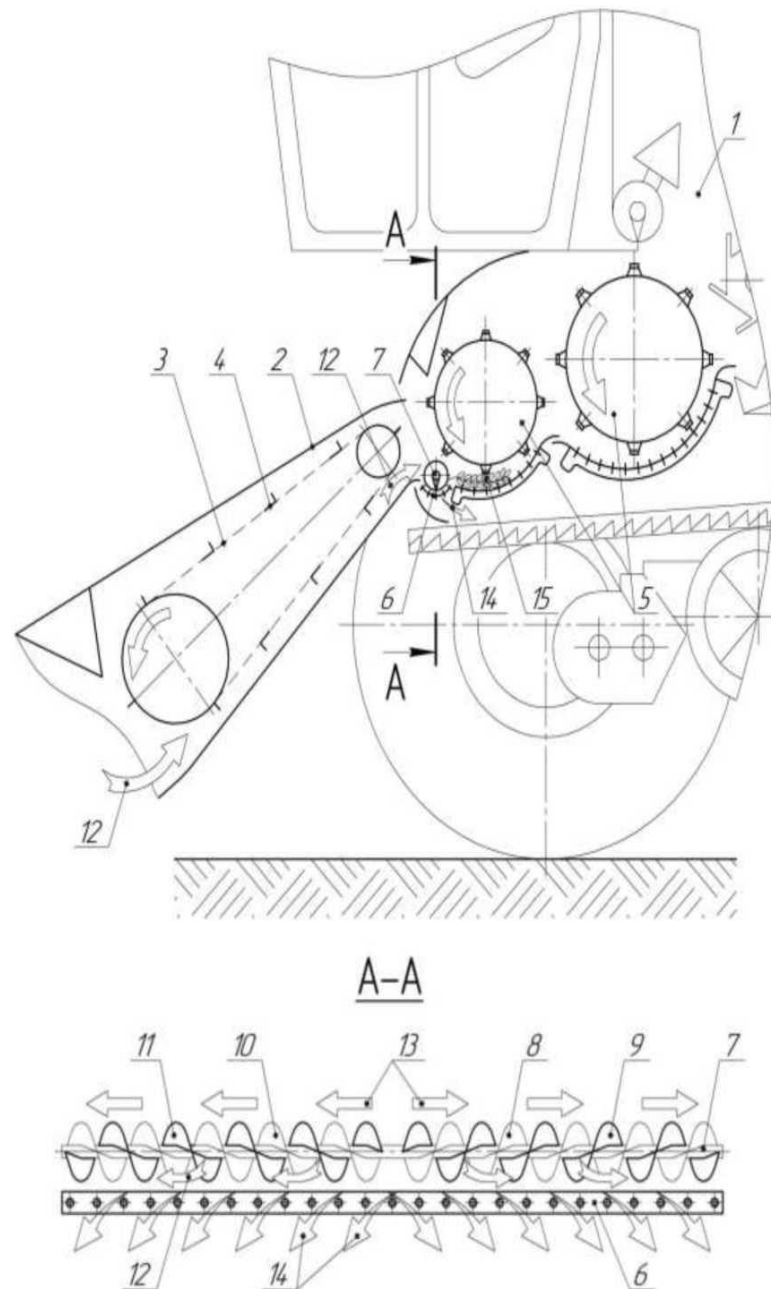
Зернозбиральний комбайн, з пристроєм для попереднього виділення вільного зерна: 1 – комбайн; 2 – похила камера; 3 – транспортер; 4 – скребок; 5 – молотарка; 6 – сепаруюча решітка; 7 – шнек; 8-11 – витки шнека; 12 – хлібна маса; 13 – напрямок руху хлібної маси; 14 – вільне зерно; 15 – колосова частина врожаю.
